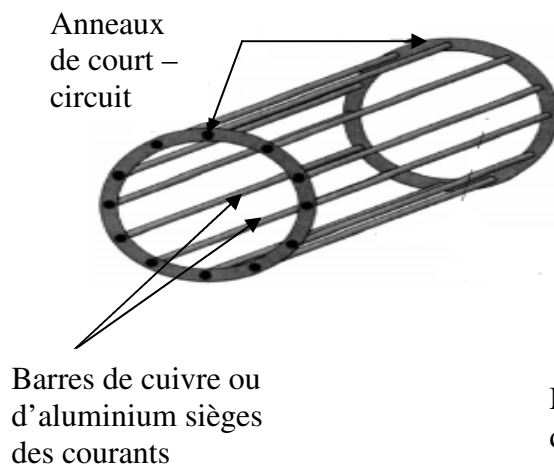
Rotor à cage d'écureuil d'une machine asynchrone [6].
